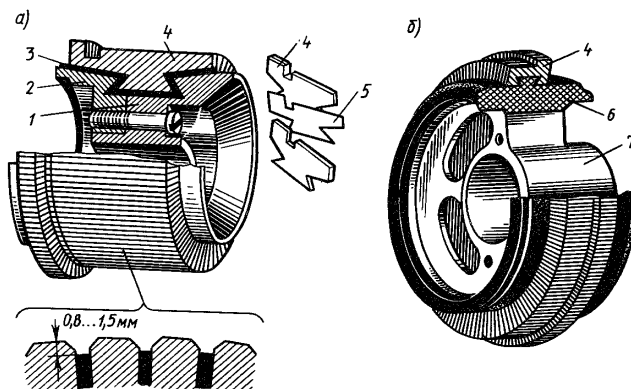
Устройство коллектора машины постоянного тока с металлическим (а) и пластмассовым (б) корпусом: 1 – корпус; 2 – нажимный фланец; 3 – изоляционные манжеты; 4 – коллекторные пластины; 5 – изоляционные прокладки; 6 – пластмасса; 7 – втулка
